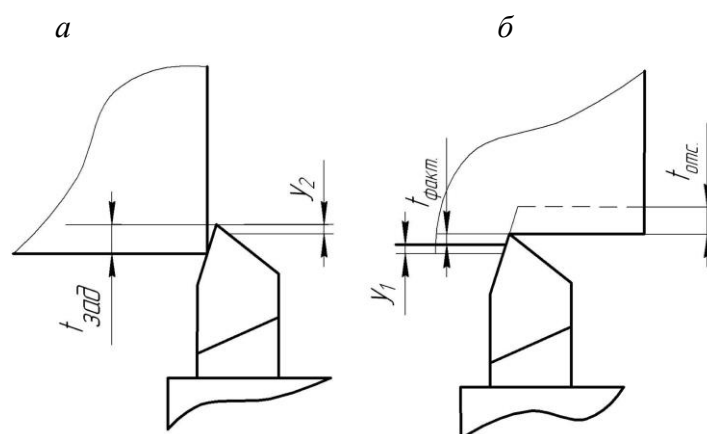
Схема к определению упругих отжатий инструмента (а) и заготовки (б)
